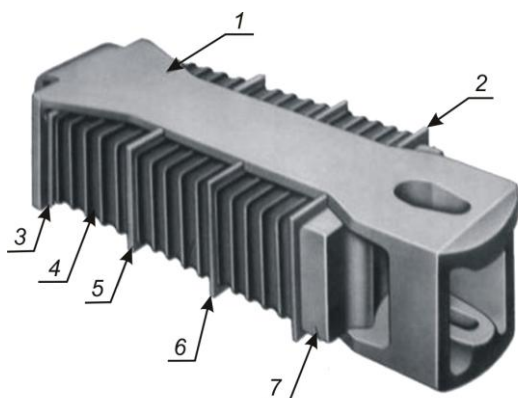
Общий вид резинометаллического поглощающего аппарата Р-5П:
